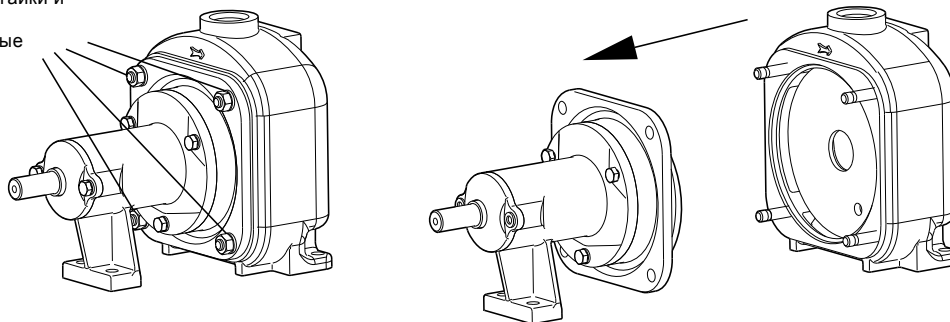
Демонтаж крышки корпуса насоса и подшипникового узла
